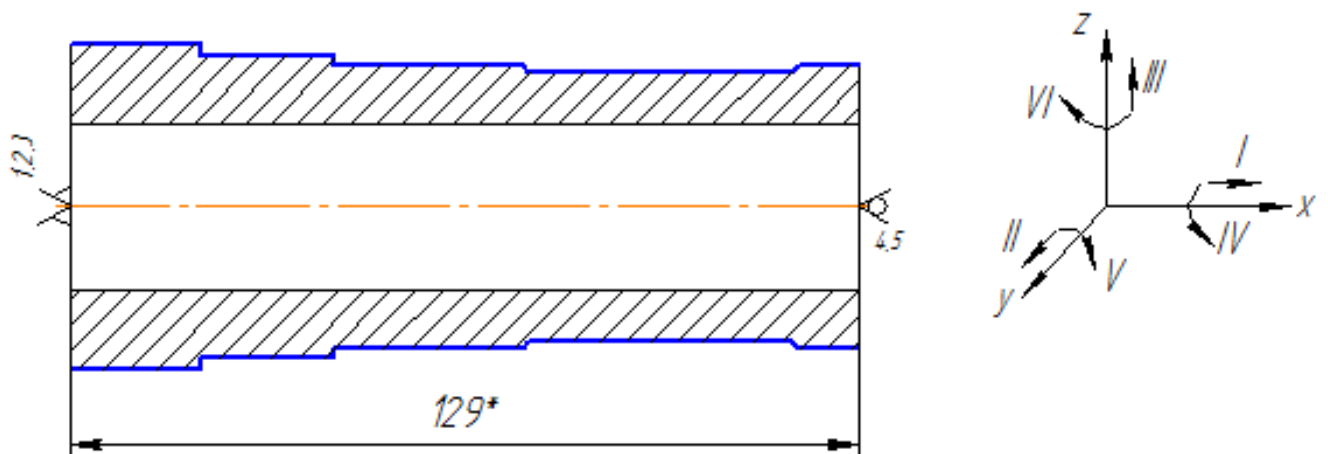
Перший спосіб базування та закріплення заготовки
